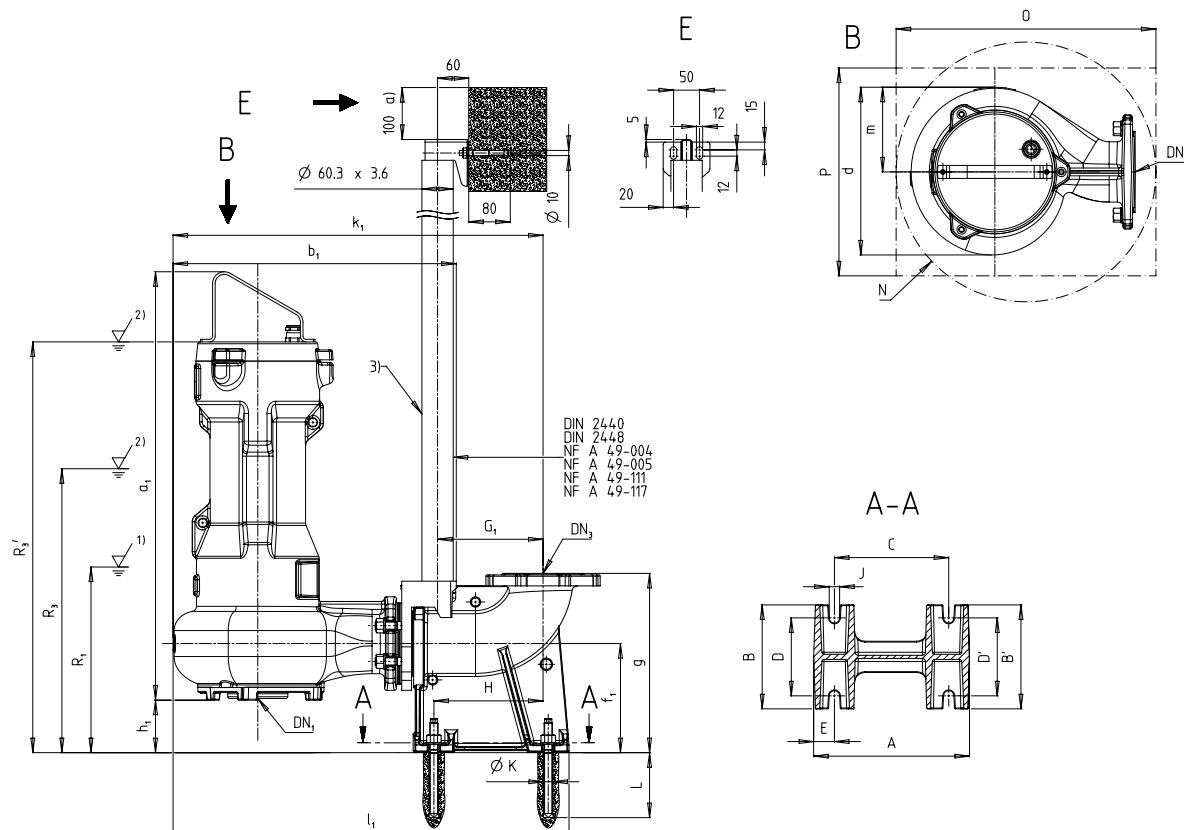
Amarex 100, installazione fissa, guida per 1 barra
